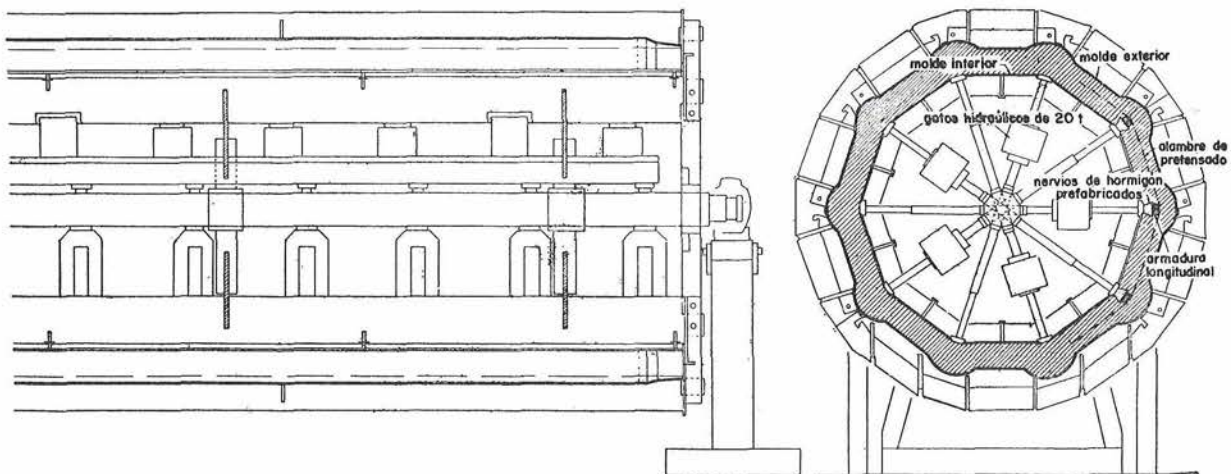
Secciones, longitudinal y transversal, de la máquina utilizada para la fabricación de las tuberías. El alambre de pretensado se sujeta, en los vértices del polígono, en unos redondos longitudinales que, a su vez, se apoyan sobre nervios de hormigón, prefabricados. La tensión se introduce mediante gatos hidráulicos de 20 toneladas, que empujan los alambres hacia el exterior.
